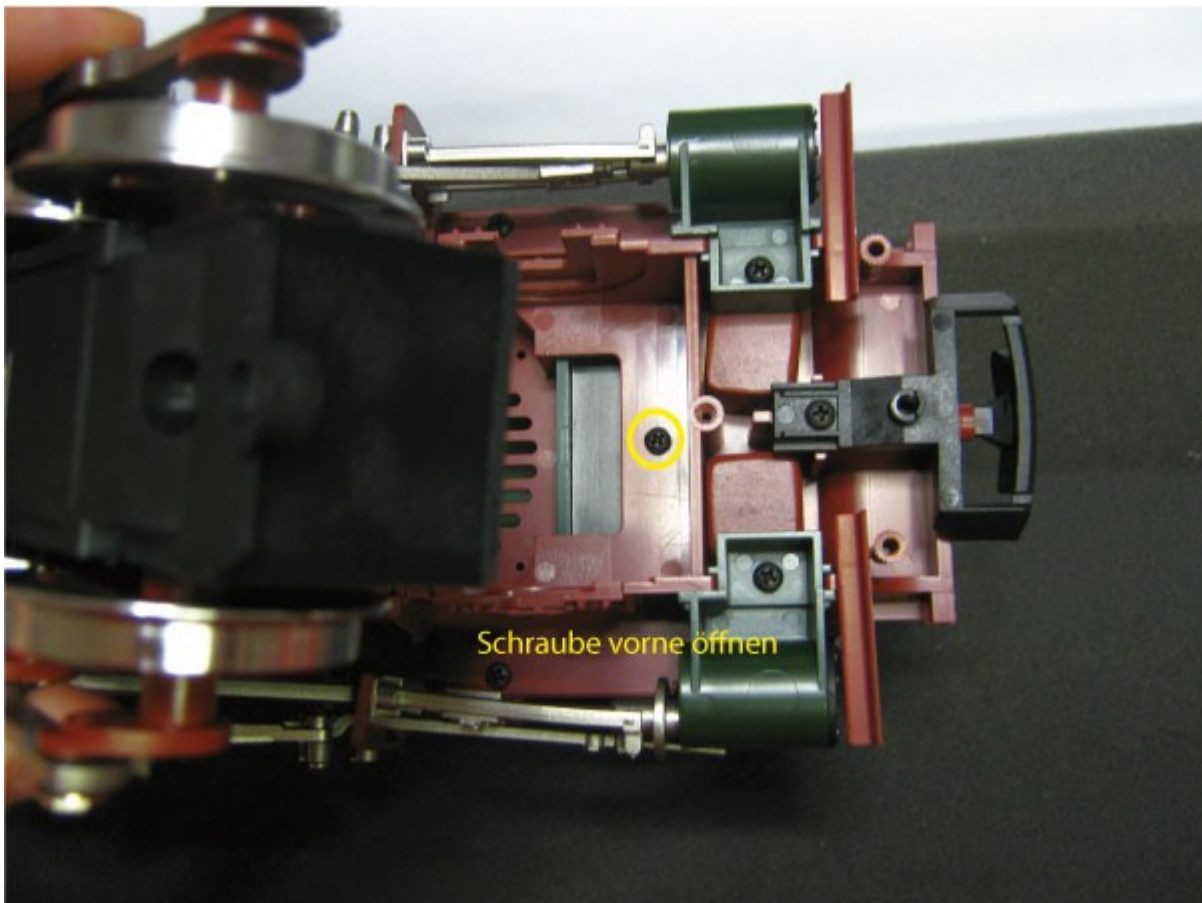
Entfernen der vorderen Schraube unter Getriebe.
